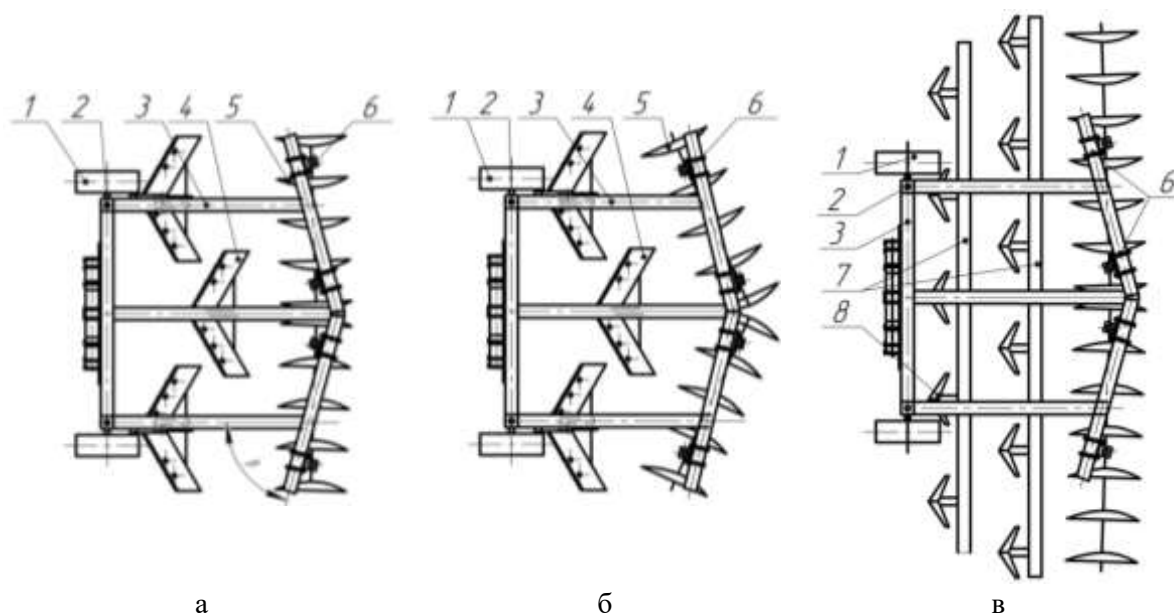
Схема размещения рабочих органов почвообрабатывающего агрегата (плоскорезущие лапы установлены по схеме «обратного» клина):
